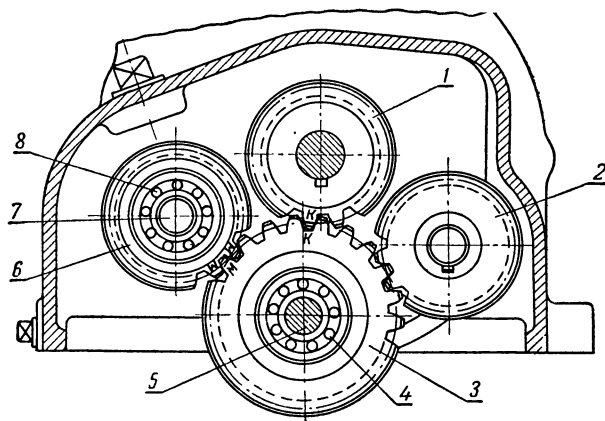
Шестерни распределения пускового двигателя: 1 — шестерня коленчатого вала; 2 — шестерня привода регулятора; 3 — промежуточная шестерня; 4 — шарикоподшипник; 5 — ось промежуточной шестерни; 6 — шестерня привода магнето; 7 — ось шестерни привода магнето; 8 — шарикоподшипник.
